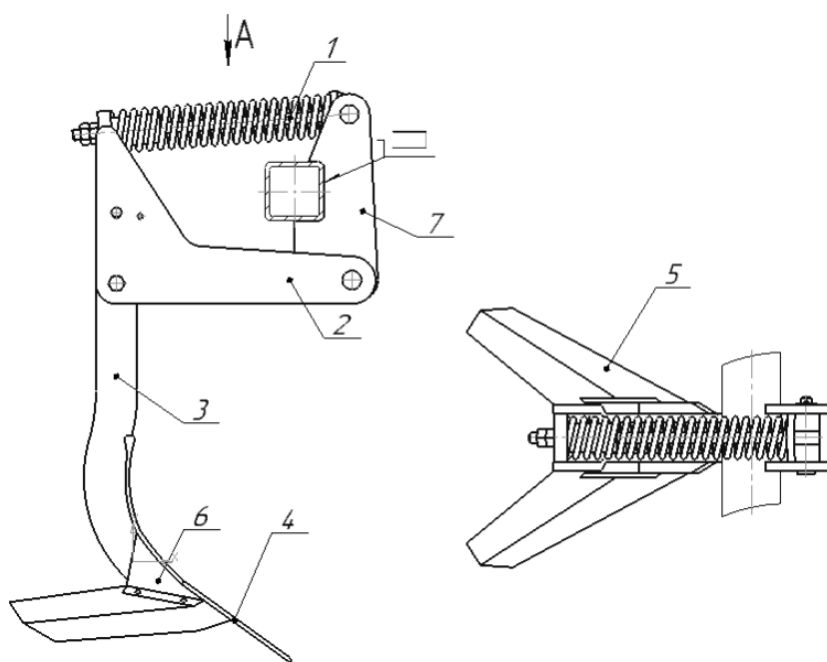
Модернизированный рабочий орган культиватора КШУ-12: 1 – пружина; 2 – рычаг; 3 – стойка; 4 – лапа рыхлительная; 5 – лемех боковой; 6 – кронштейн бокового лемеха; 7 – кронштейн рычага
